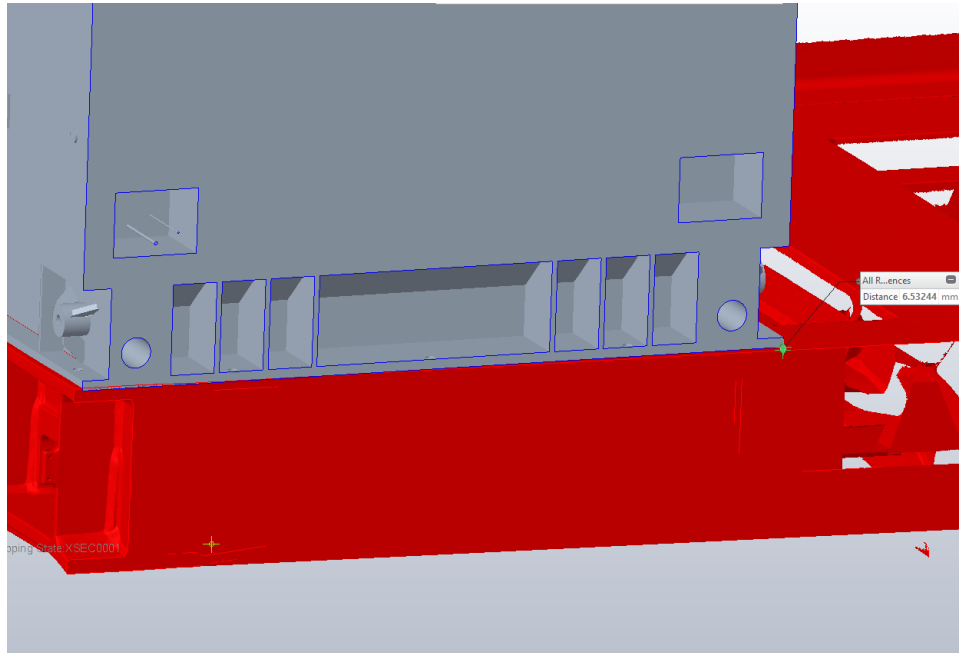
3d-skannad plattform med basplatta till framdrivningsmotor (blå) och Stirling modul (grå)
